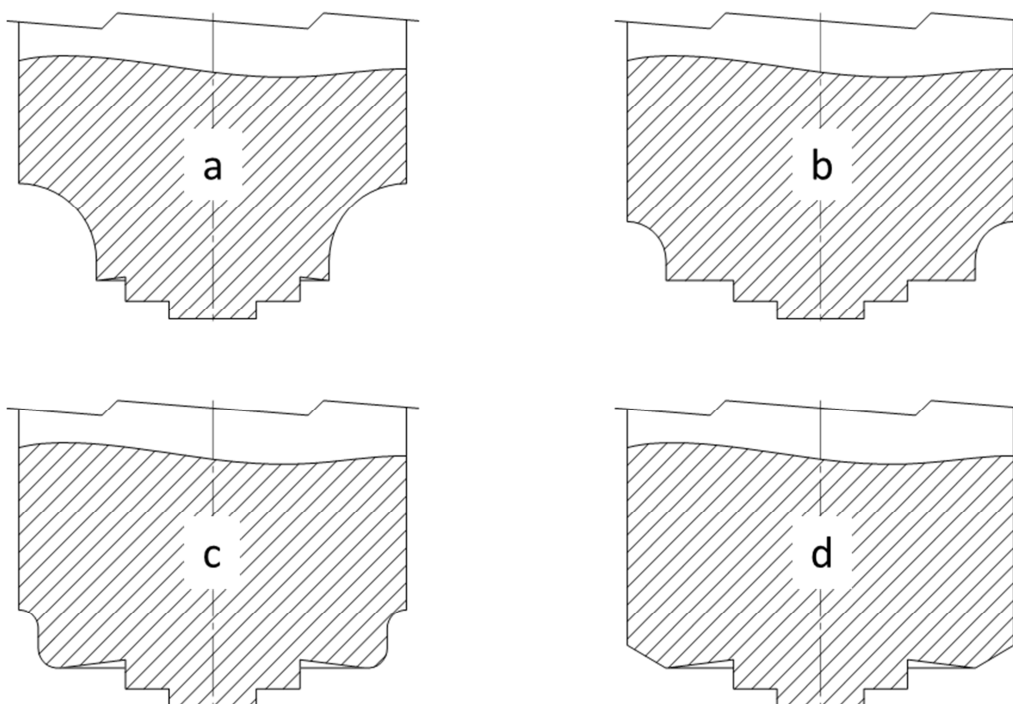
Untersuchte Werkzeugvarianten a-d
